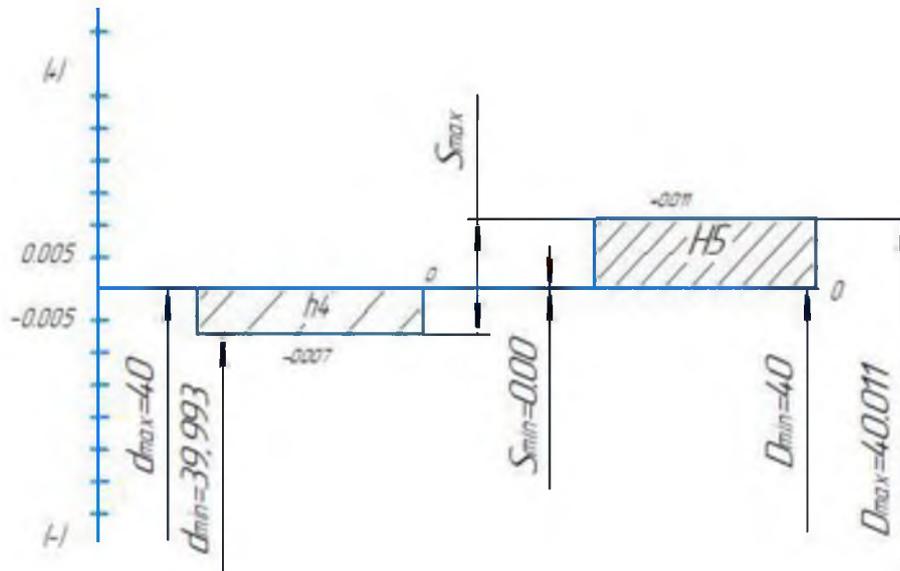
Схема расположения полей допусков в система вала
